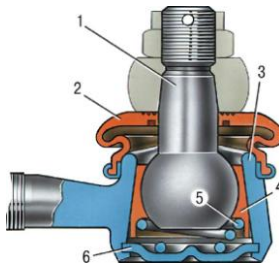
Кульовий шарнір тяги: 1 - кульовий палець; 2 – ковпачок (пильник); 3 - корпус шарніра; 4 - вкладиш; 5 - пружина; 6 – заглушка.
